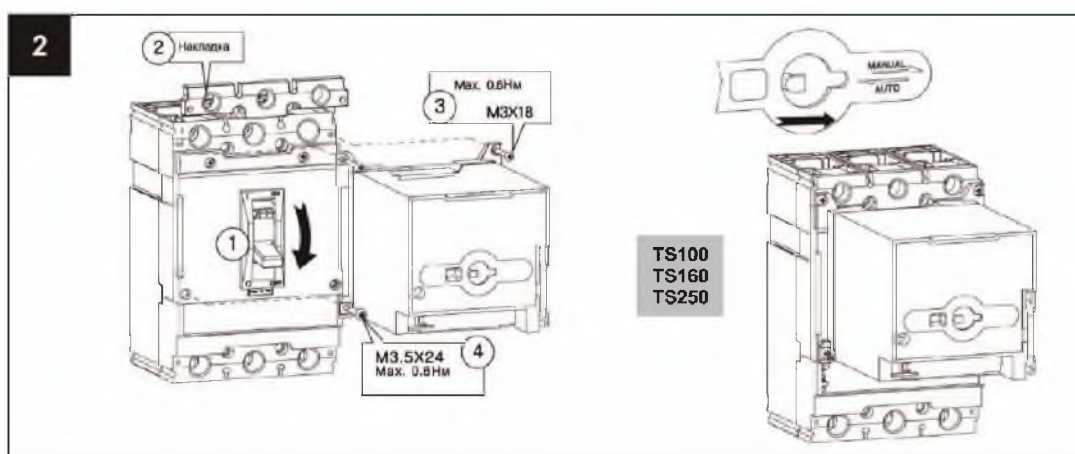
Установка моторного привода на выключатели TS100-TS250
